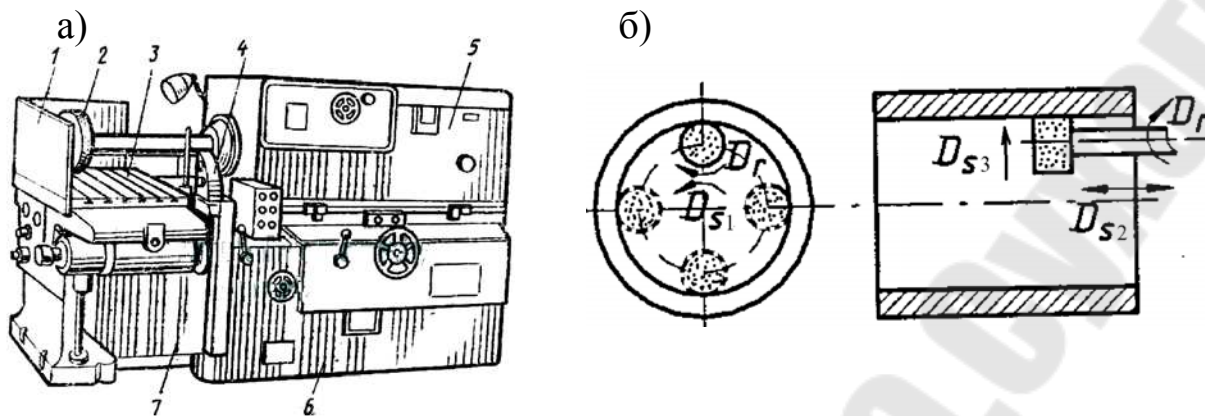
Общий вид внутришлифовального планетарного станка (а) и схема планетарного шлифования отверстия (б)
